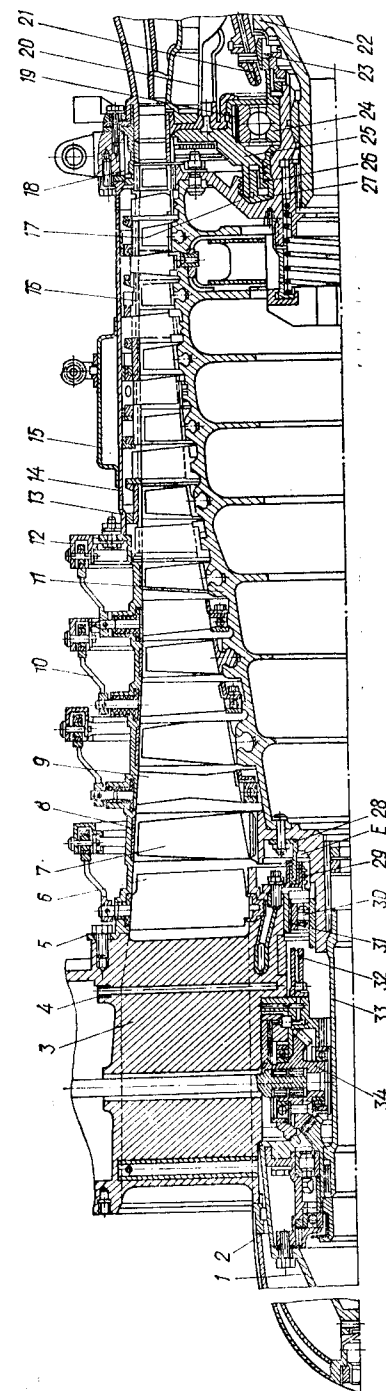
Конструкция компрессора: 1 — крышка; 2 — профилированный кок; 3 — корпус первой опоры; 4 — жиклер; 5 — передний корпус; 6 — лопатки ВНА; 7 — рабочее колесо I ступени; 8 — слой масла; 9 — поворотные лопатки; 10 — рычаги; 11 — центральная часть ротора; 12 — поворотные полукольца; 13 — средний корпус; 14 — наружная обечайка среднего корпуса; 15 — кольцевая коробка; 16 — рабочее колесо X ступени; 17 — лопатки ВНА; 18 — задний корпус; 19, 31 — упругий элемент; 20 — корпус лабиринтов; 21, 32 — форсунки; 22, 27, 28 — гребешковые лабиринты; 23, 26, 29 — контактно-кольцевые уплотнения; 24 — шарикоподшипник второй опоры; 25 — корпус второй опоры; 26 — роликподшипник первой опоры; 33 — рессора центрального привода; 34 — привод коробки привода
